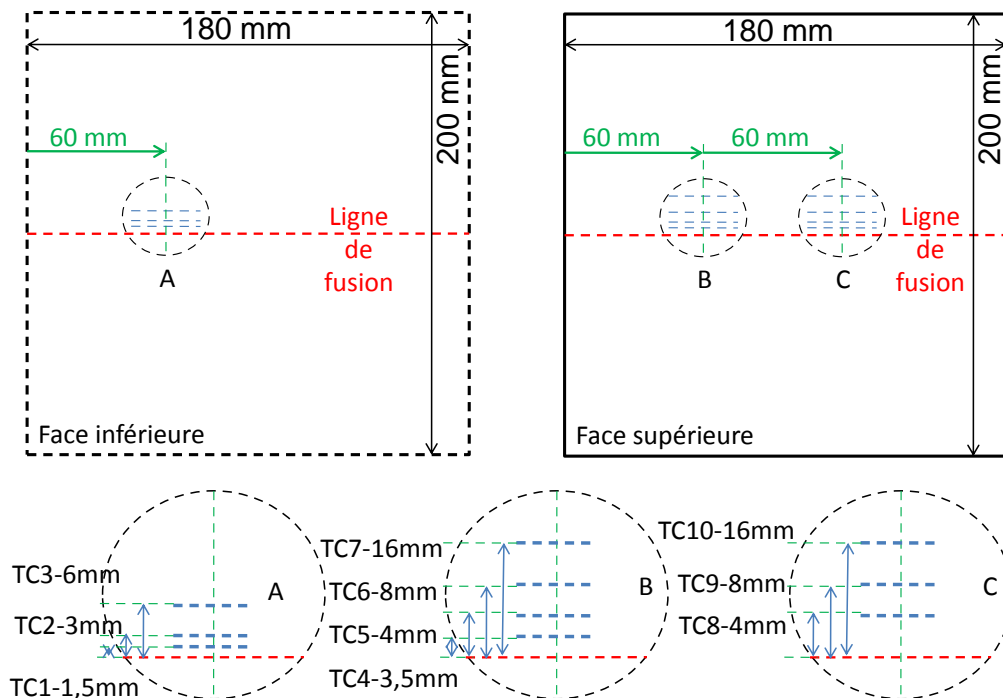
Positions des thermocouples sur la plaque soudée à 0,45 m/min
